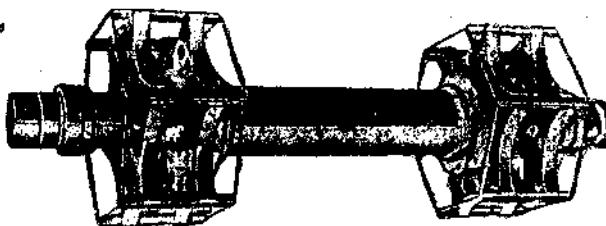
Инструмент Hutto для золотниковой коробки паровоза.
